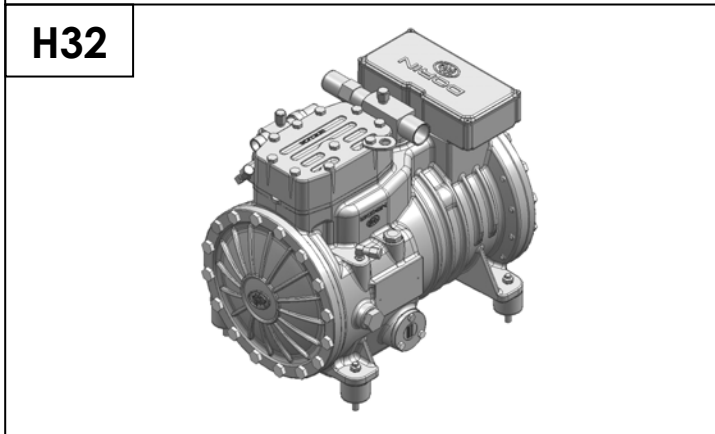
Istruzioni montaggio resistenza carter - Mounting instructions
